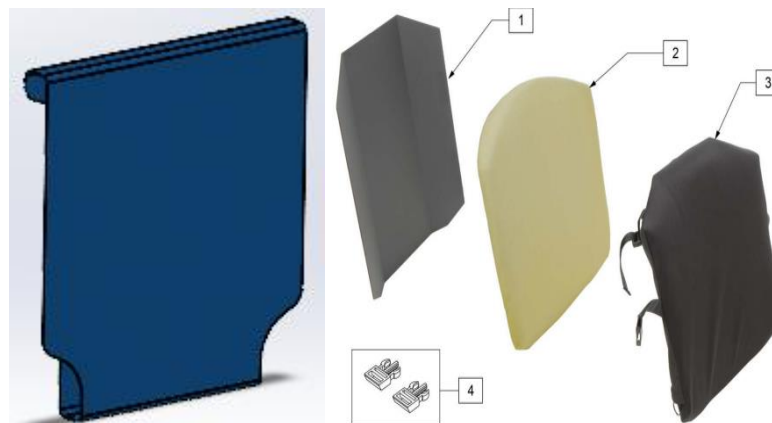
Tapicería de nylon elástico recubierta del respaldo
